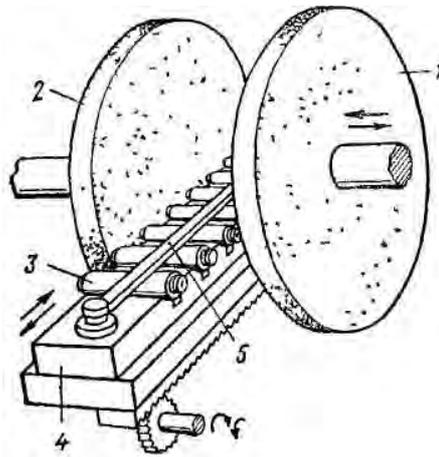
Схема специального станка для двустороннего шлифования торцов пружин
